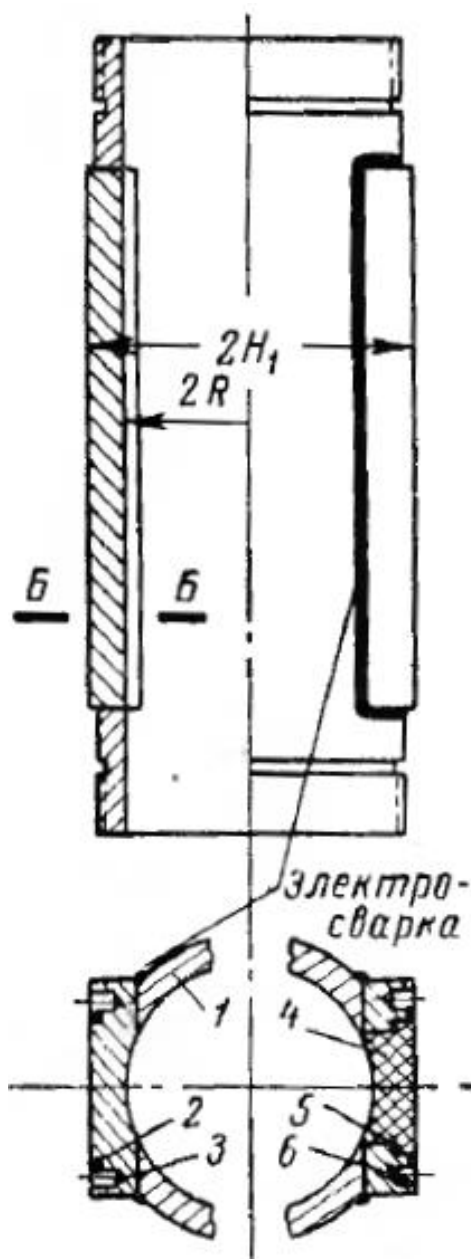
Схематический чертеж корпуса преобразователя с двумя преломляющими поверхностями с плоской внешней преломляющей поверхностью при диаметрах трубопровода менее 100 мм
